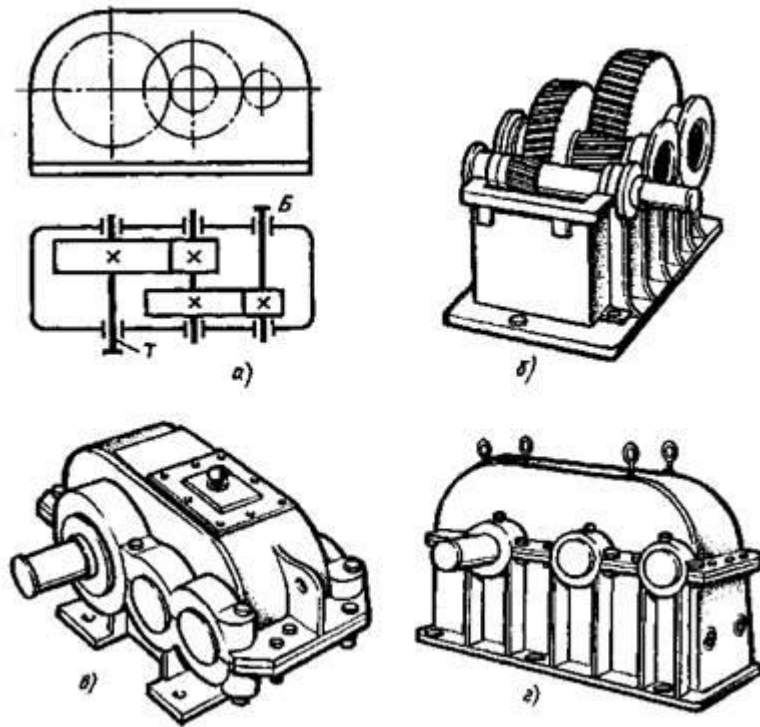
Двоступеневий горизонтальний редуктор з циліндричними колесами типу Ц2-750: а – кінематична схема; б – редуктор зі знятою кришкою (колеса косозубі); в – загальний вигляд редуктора, у якого підшипникові вузли закриті врізаними кришками; г – загальний вигляд редуктора, у якого підшипникові кришки прикручені гвинтами [4]
